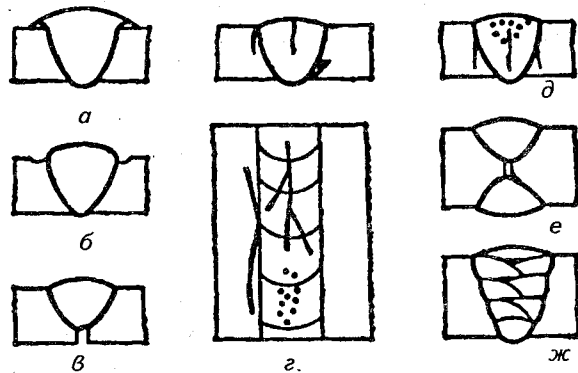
Виды дефектов в сварных соединениях: а — наплыв; б — подрез; в — непровар; г — наружные трещины и поры; д — внутренние трещины и поры; е — внутренний непровар; ж — шлаковые включения
